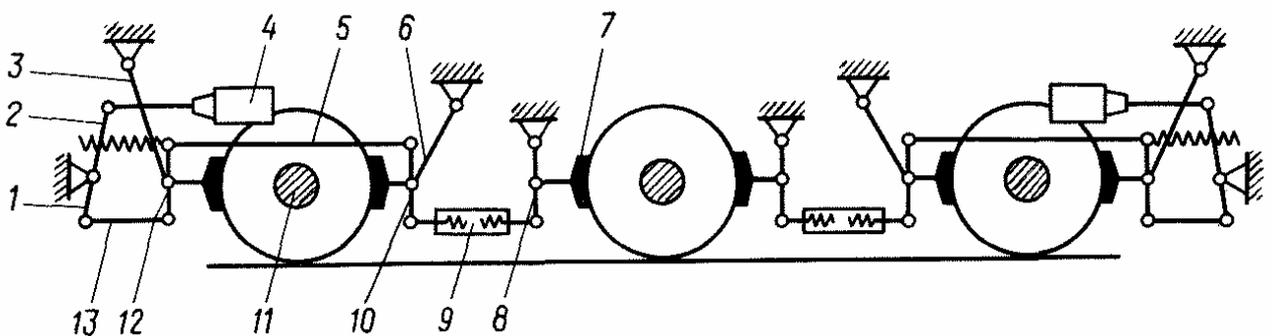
Кинематическая схема тормозной рычажной передачи ЧМЭЗ
